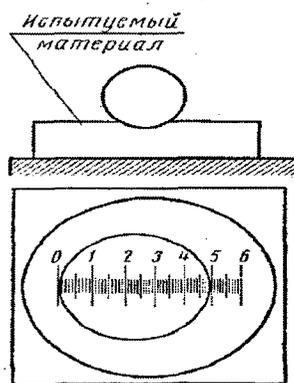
Схема испытания металлов на твердость вдавливанием стального шарика и измерением отпечатка
